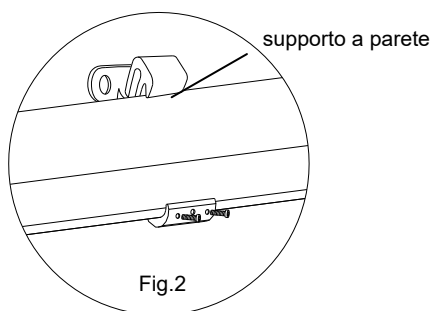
Suggestire a due persone di sollevare la tenda da sole (A) all'altezza del supporto a parete e di far scorrere la tenda da sole (A) nel supporto a parete (B), collegare il supporto a parete (B) e la parte di collegamento (C) sulla tenda da sole (A) tramite il bullone (AA); ciascuna distanza tra le due è di 2115 mm (83,3 pollici).
